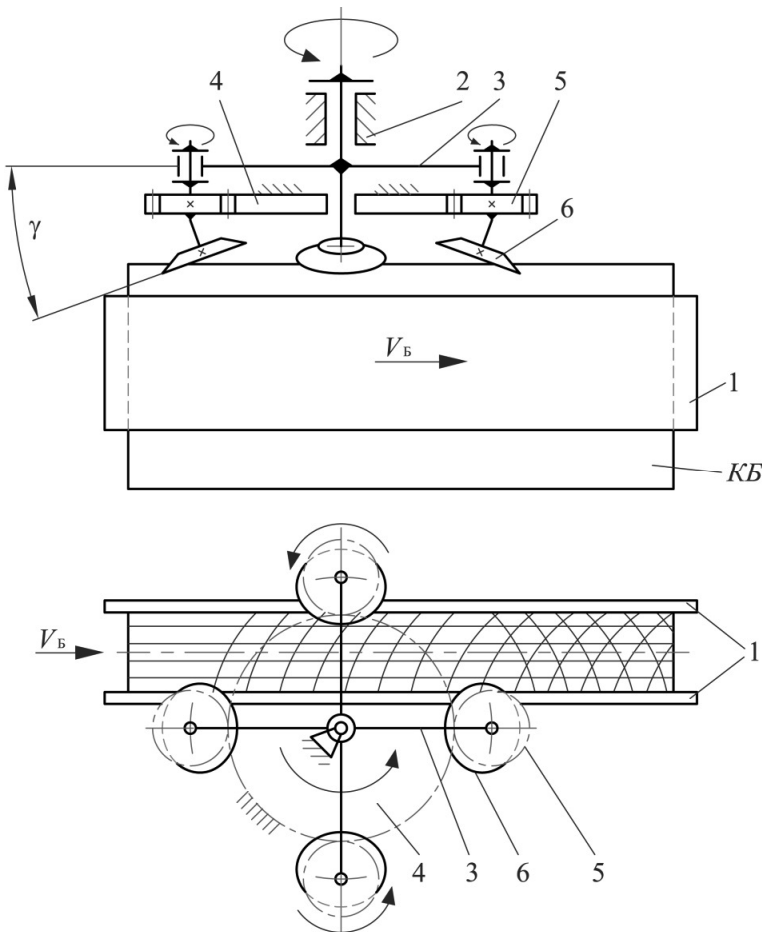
Принципова схема способу обробки кінця книжкового блока дисковими ножами з планетарним приводом
